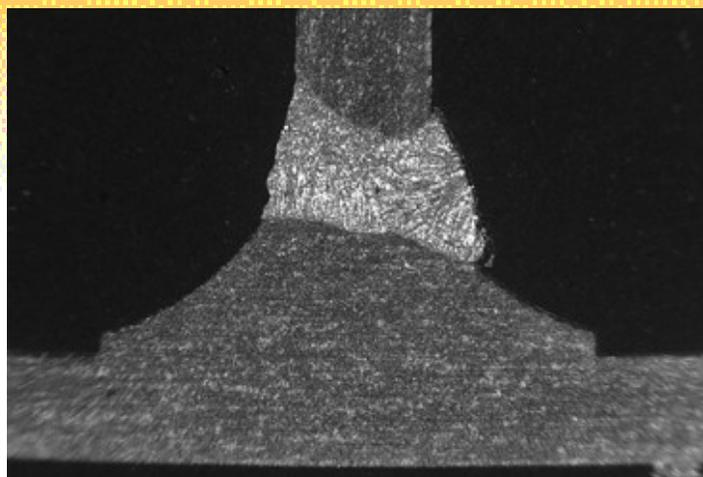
soudure HLW bout-à-bout d'aluminium série 5xxx (1,8 mm) configuration à 7,8 m/min
